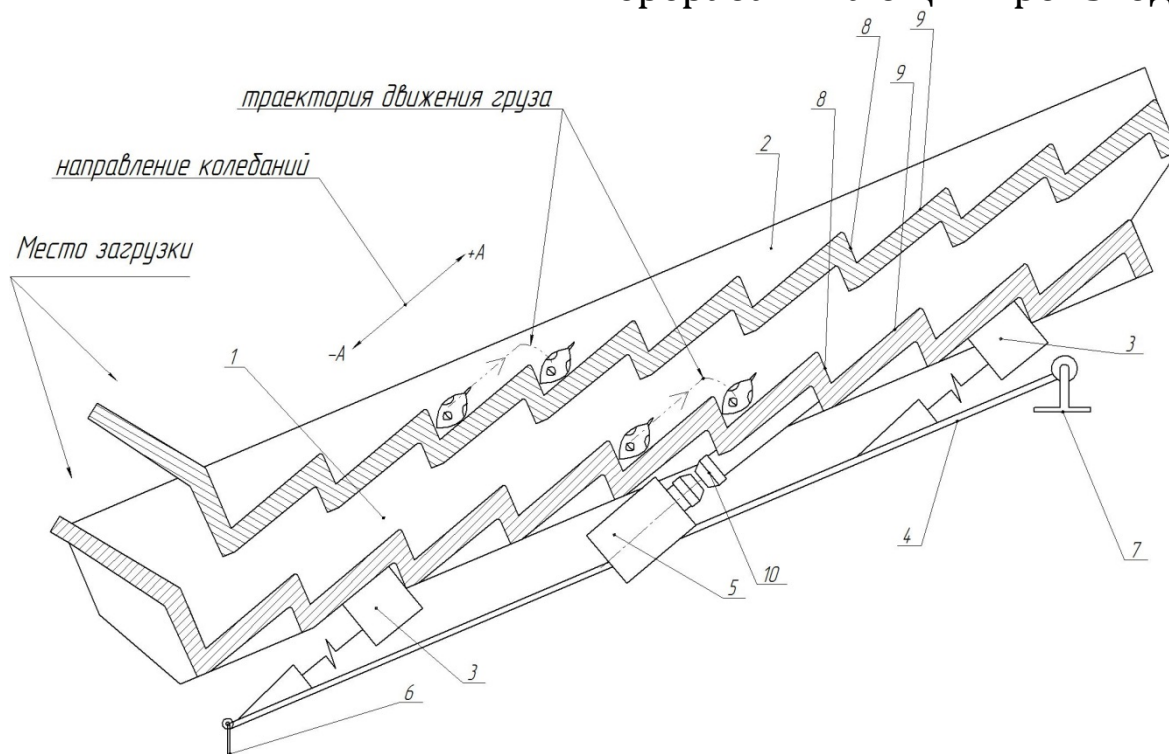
Схема конструкции вибрационного конвейера с двумя ступенчатыми рабочими поверхностями
